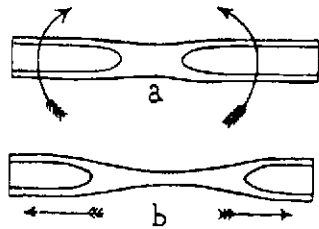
Préparation d'un tube effilé pour couper un gros tube.
